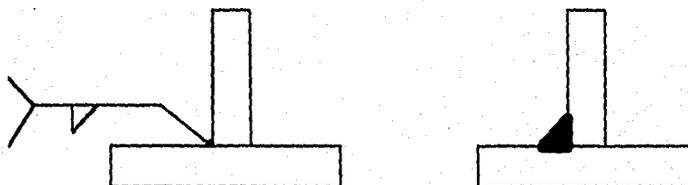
Aplicación de la soldadura únicamente del lado derecho
